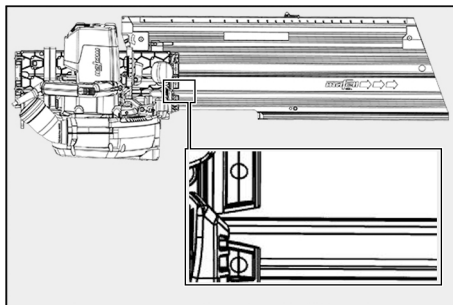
Colocar la máquina en el dispositivo guía KSS
